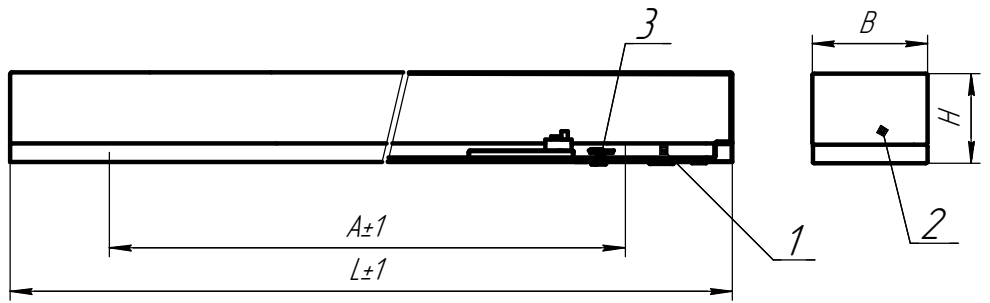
ДПО46-19; 38; 76 1. корпус в сборе; 2. рассеиватель; 3. зажим
